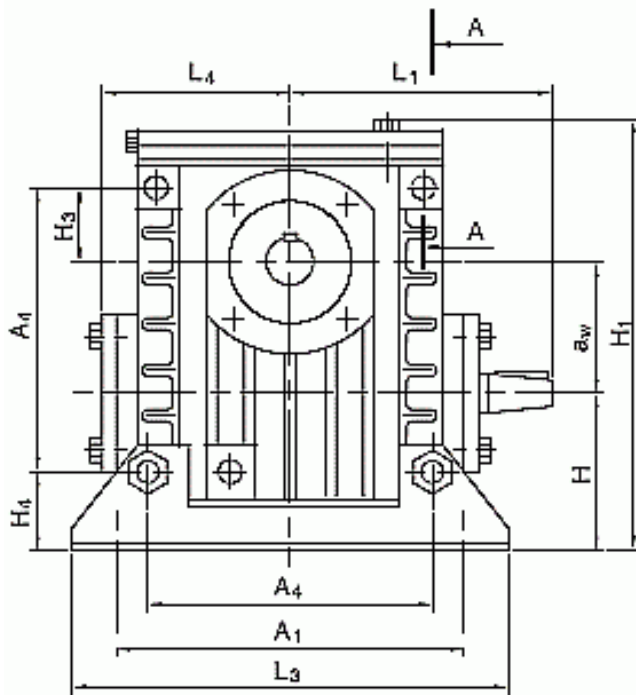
Общий вид, габаритные и присоединительные размеры червячного редуктора 2Ч-80 [18]
